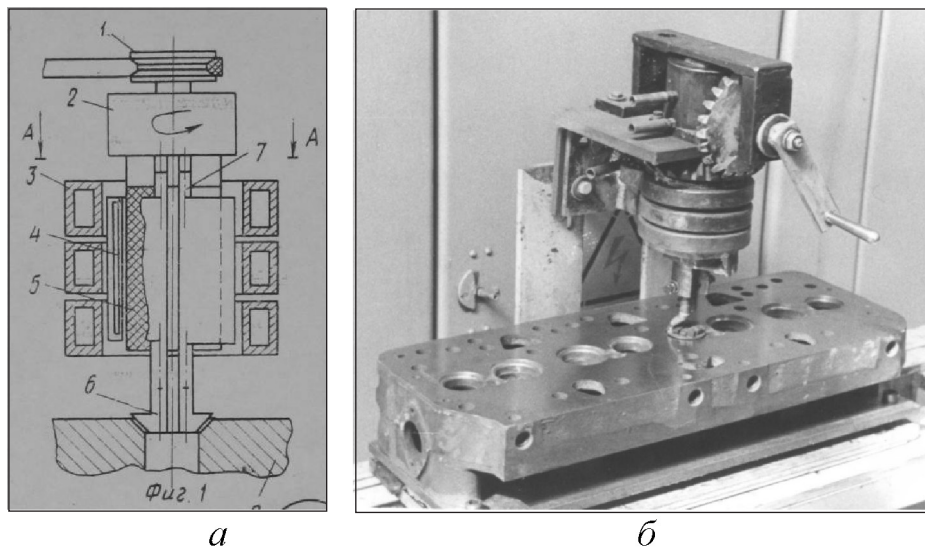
Устройства для закалки гнезд клапанов головки блока цилиндров трактора МТЗ:
